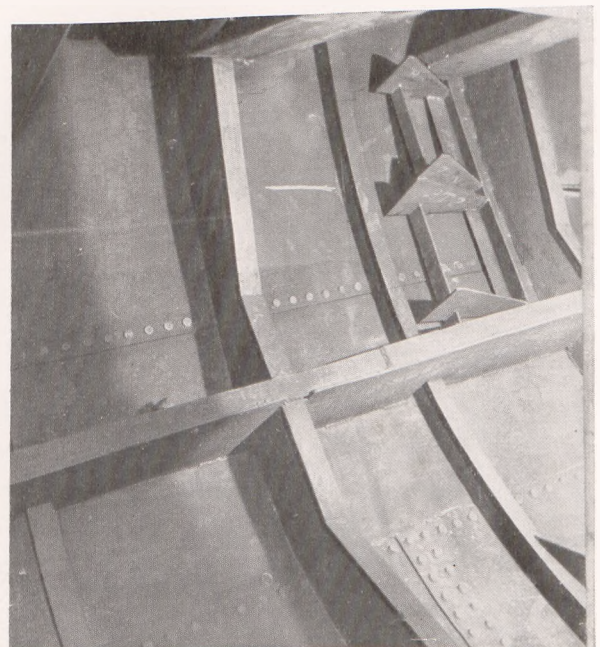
Bordwand im Motorenraum mit geschweißten Spanten, Rahmenspanten, Längsträgern und Konsolen.
